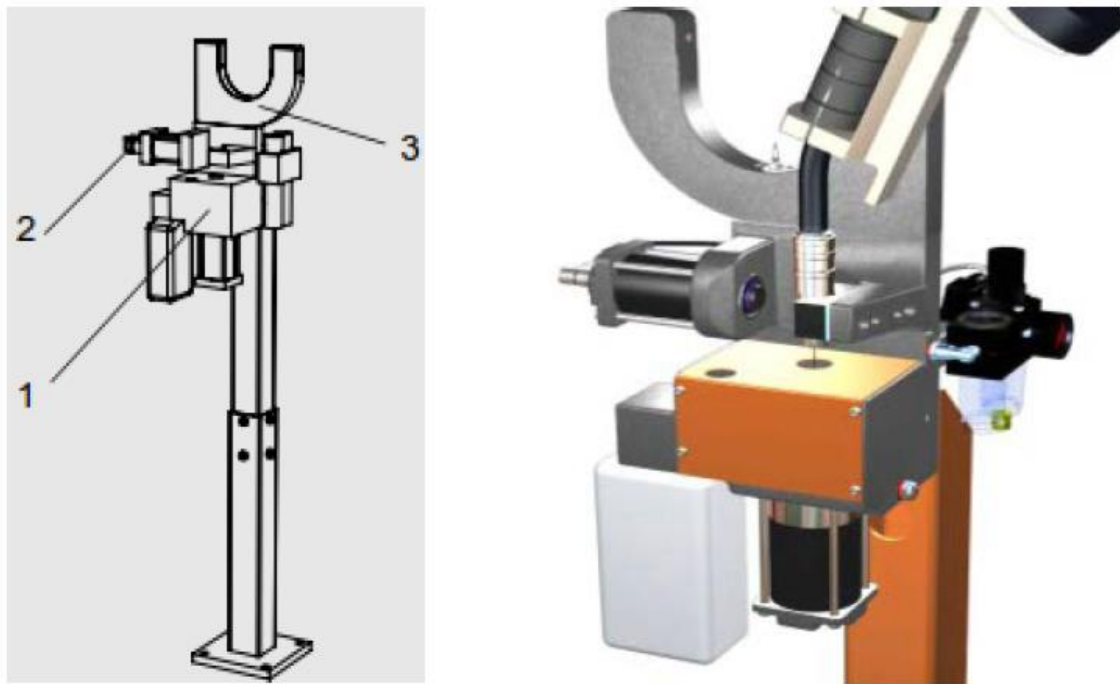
Станція очищення сопла зварювального пальника TSC: 1 – очищувач сопла; 2 – кусачки для зварювального дроту; 3 – блок вимірювання (калібрувальний блок)
